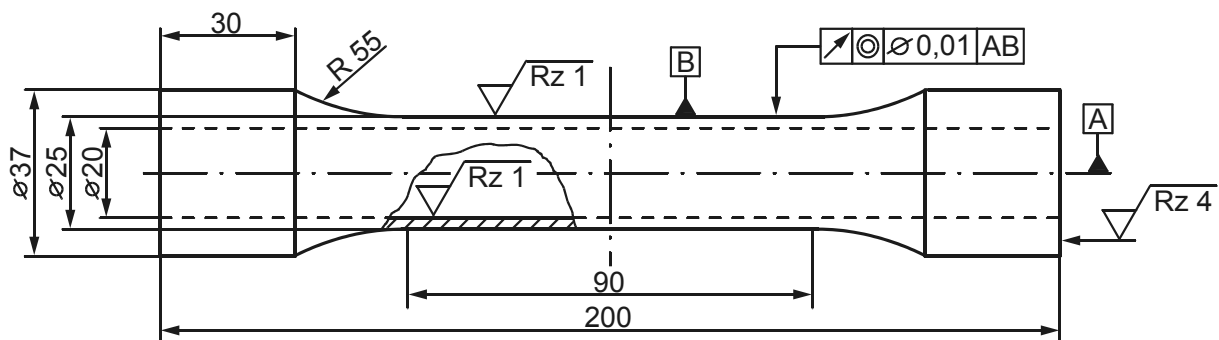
Geometrieabmessung einer Hohlzylinderprobe
